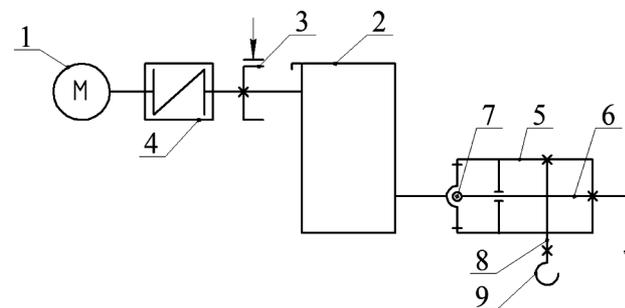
Кинематическая схема механизма подъема мостового крана: 1 – электродвигатель; 2 – редуктор; 3 – тормоз колодочный с электромагнитом; 4 – муфта типа МУВП (с тормозным шкивом); 5 – барабан; 6 – ось (или вал) барабана; 7 – опоры барабана; 8 – грузовой канат; 9 – крюковая подвеска
